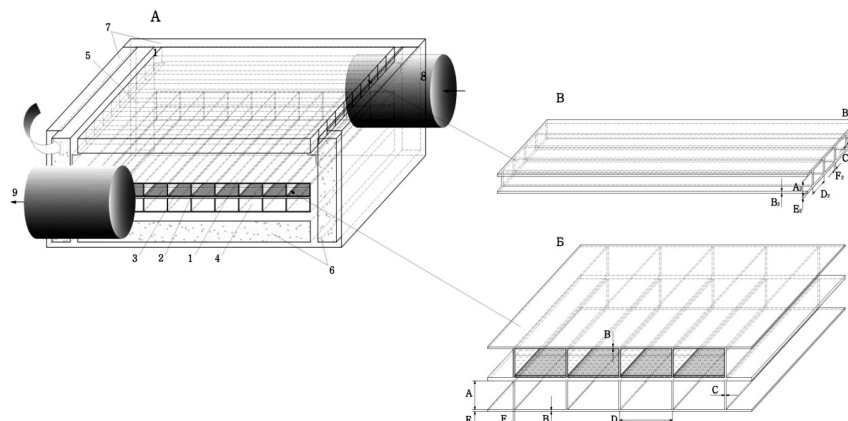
Схема полімерного сонячного колектора ПСК-ВС2-2:
